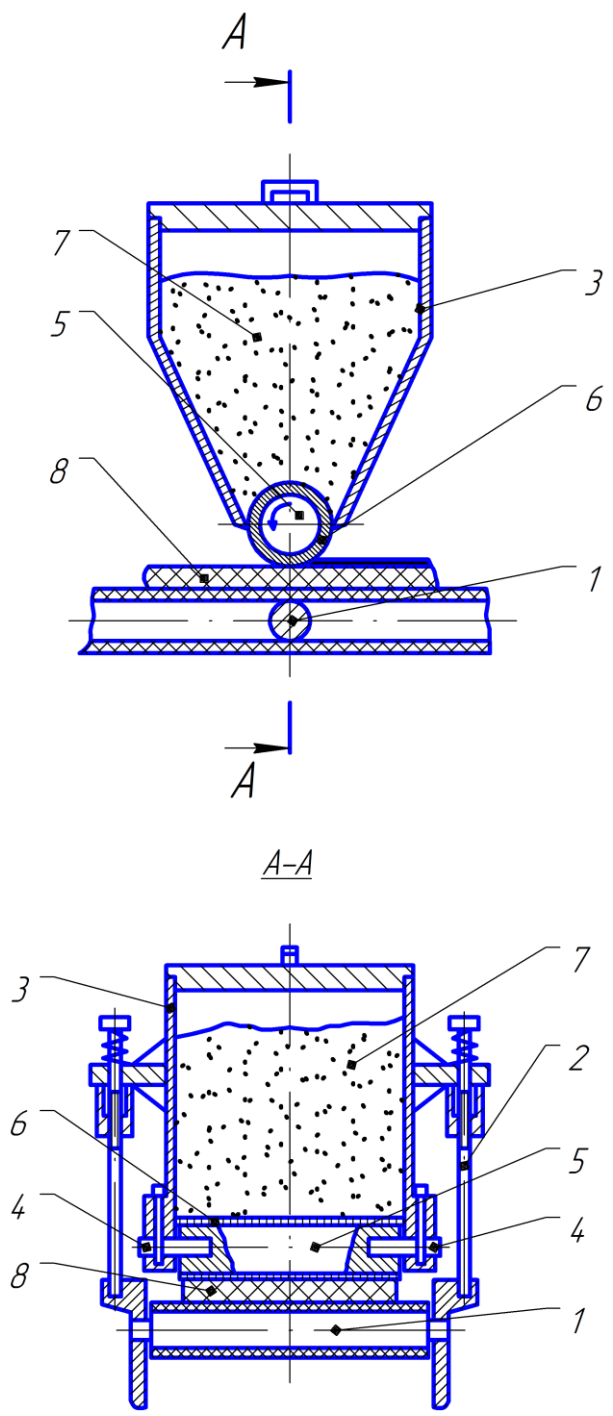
Бункерно-загрузочное устройство для нанесения талька на плоский прокат
